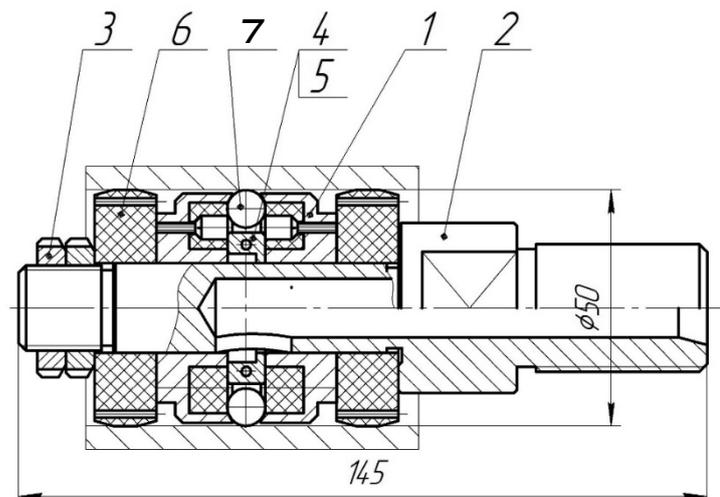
Конструктивная схема инструмента для упрочняющей обработки пневмоударом поверхностей отверстий
